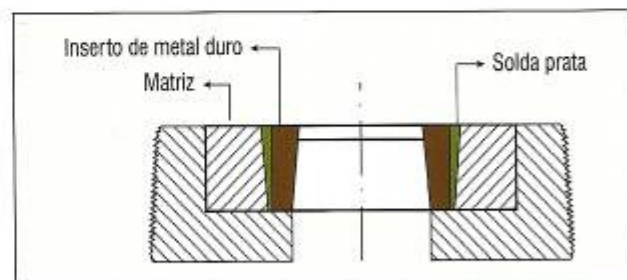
Inserto de metal duro em matriz de estampagem com solda prata
